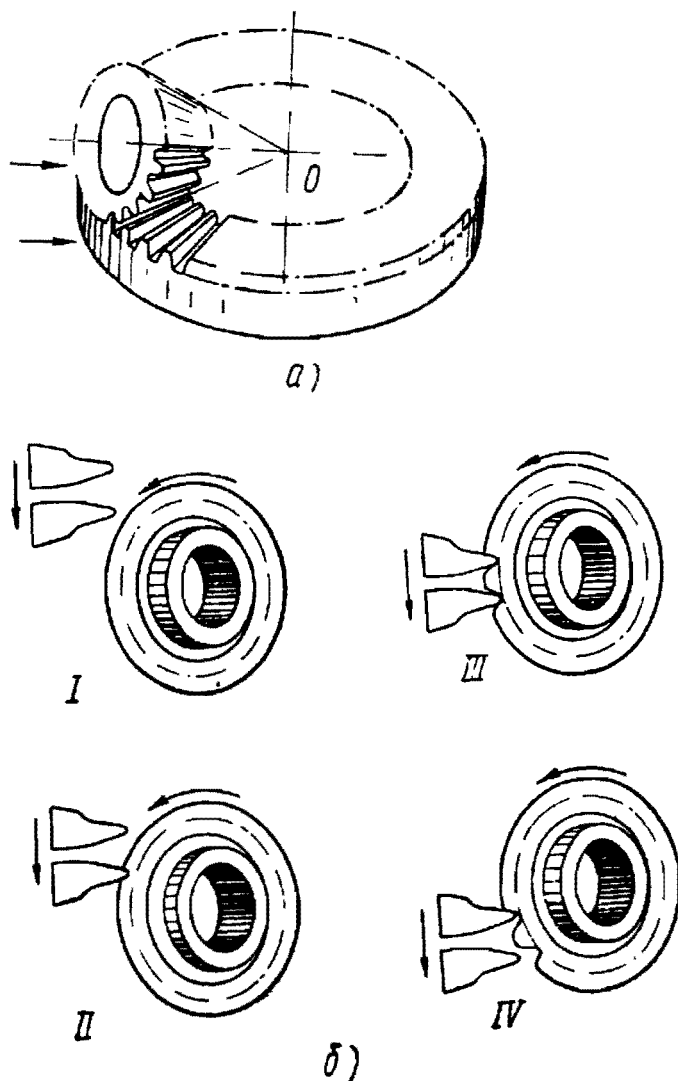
Схема нарезания конических зубчатых колес зубострогальными резцами:
